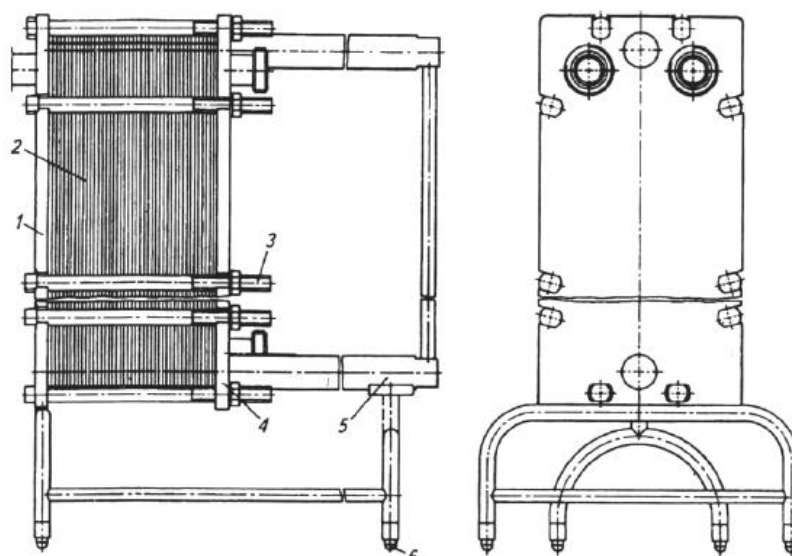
Пластинчатый аппарат установки А1-ОНС-25:
